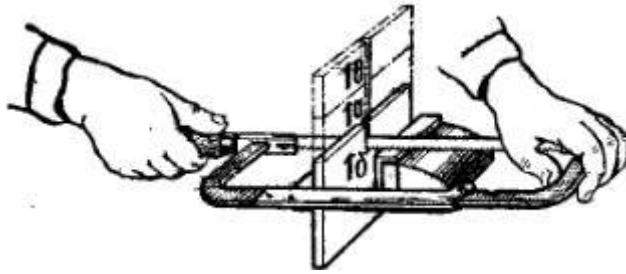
Приемы резания металла ручной слесарной ножовкой с поворотом ножовочного полотна
